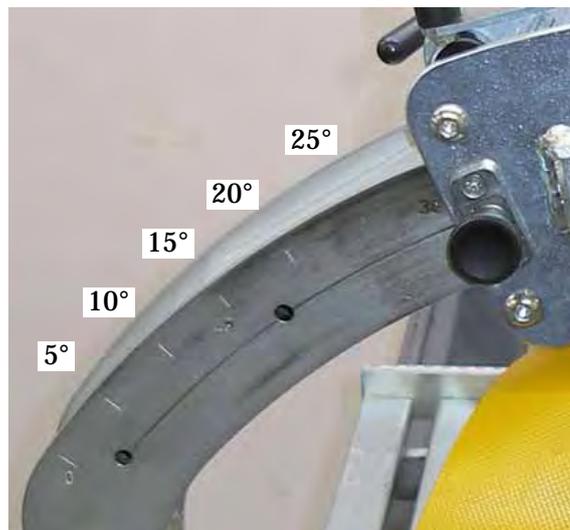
, Gehrungswinkel, 5° Markierung (Ausschnitt)
